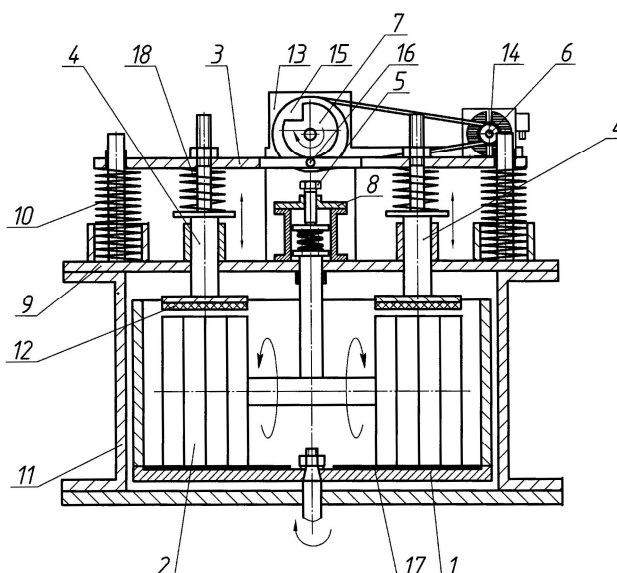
Схема катково-тарельчатой мельницы с неравномерным движением катков:
